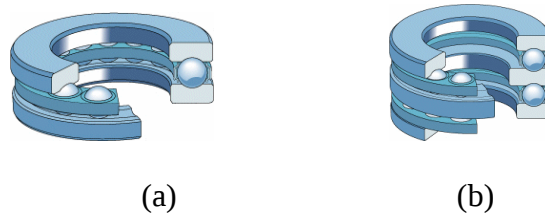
Rodamientos axiales de bolas, (a) de simple efecto, (b) de doble efecto [28].
